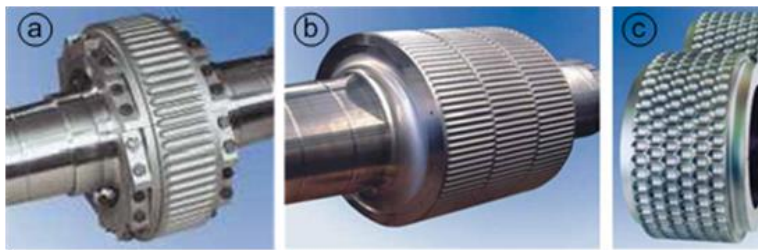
Walzen: (a - Segmente; b - Vollwalzen; c - Walzenringe)
